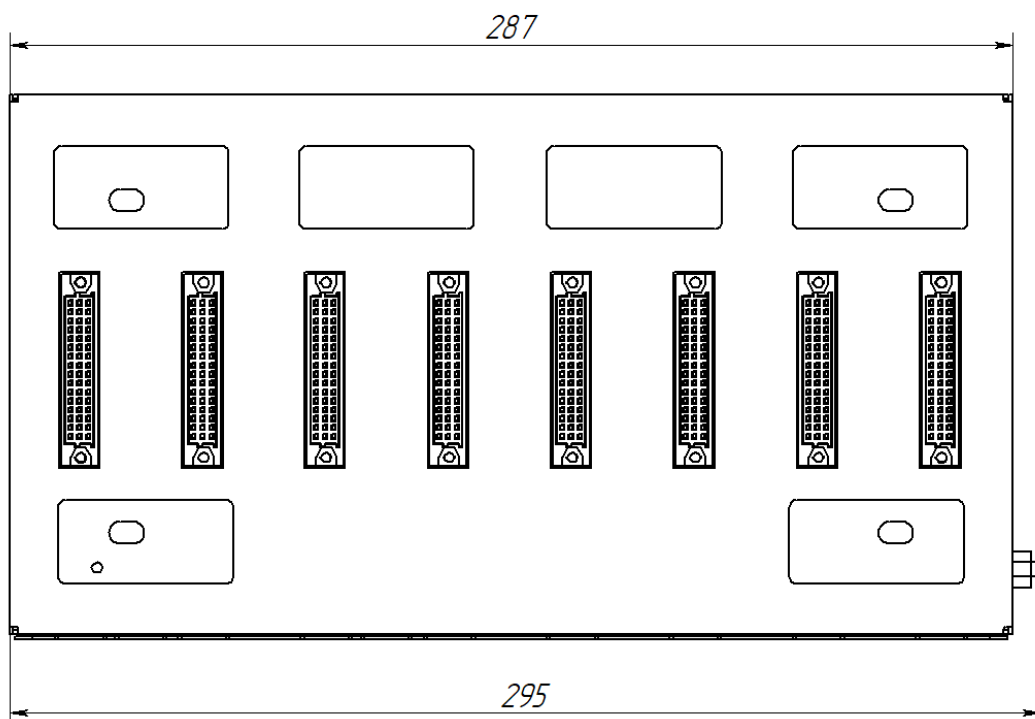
Габаритные и присоединительные размеры шасси SH-08
